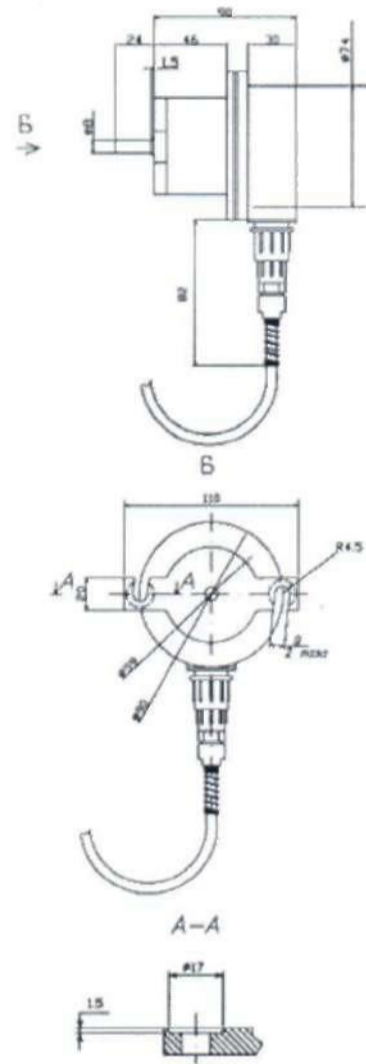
Габаритные и присоединительные размеры ДПИ
